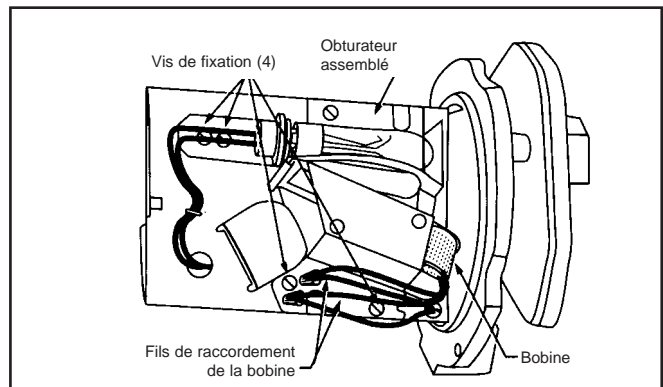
Remplacement de l'ensemble bobine et obturateur sur la C7061A.
